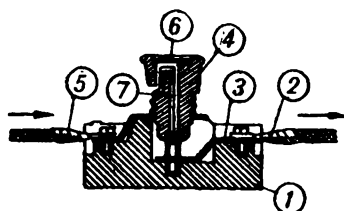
Предохранительная пробка в разрезе: 1 — фарфоровый корпус; 2 — вывод осветительного шнура; 3 — выводной контакт; 4 — корпус плавкого предохранителя; 5 — ввод осветительного шнура; 6 — стеклянное окошко; 7 — нить плавкого предохранителя.
